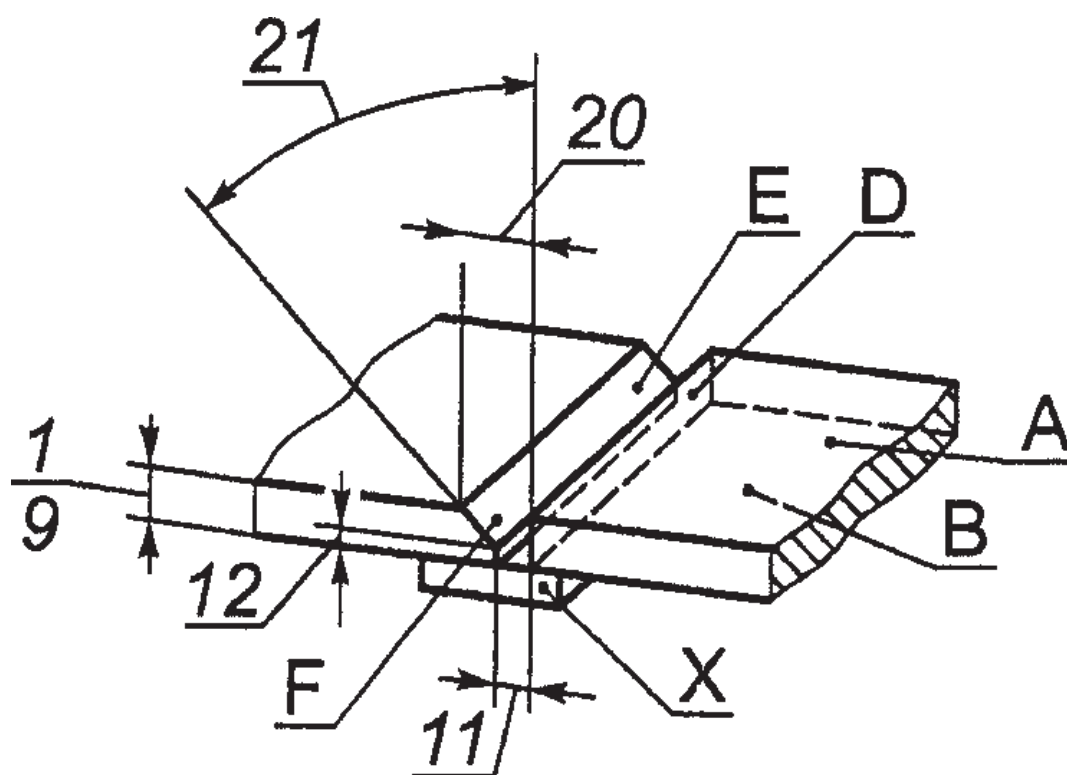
Подготовка под сварку стыкового соединения со скосом одной кромки с притуплением и с подкладкой Figure 3.
